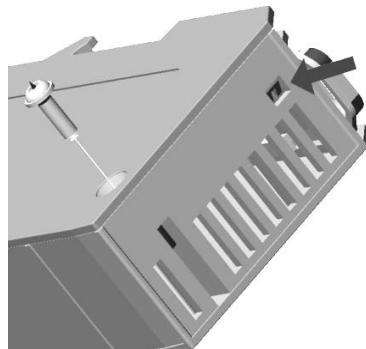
Modul öffnen: Schraube lösen und Gehäusedeckel entriegeln
